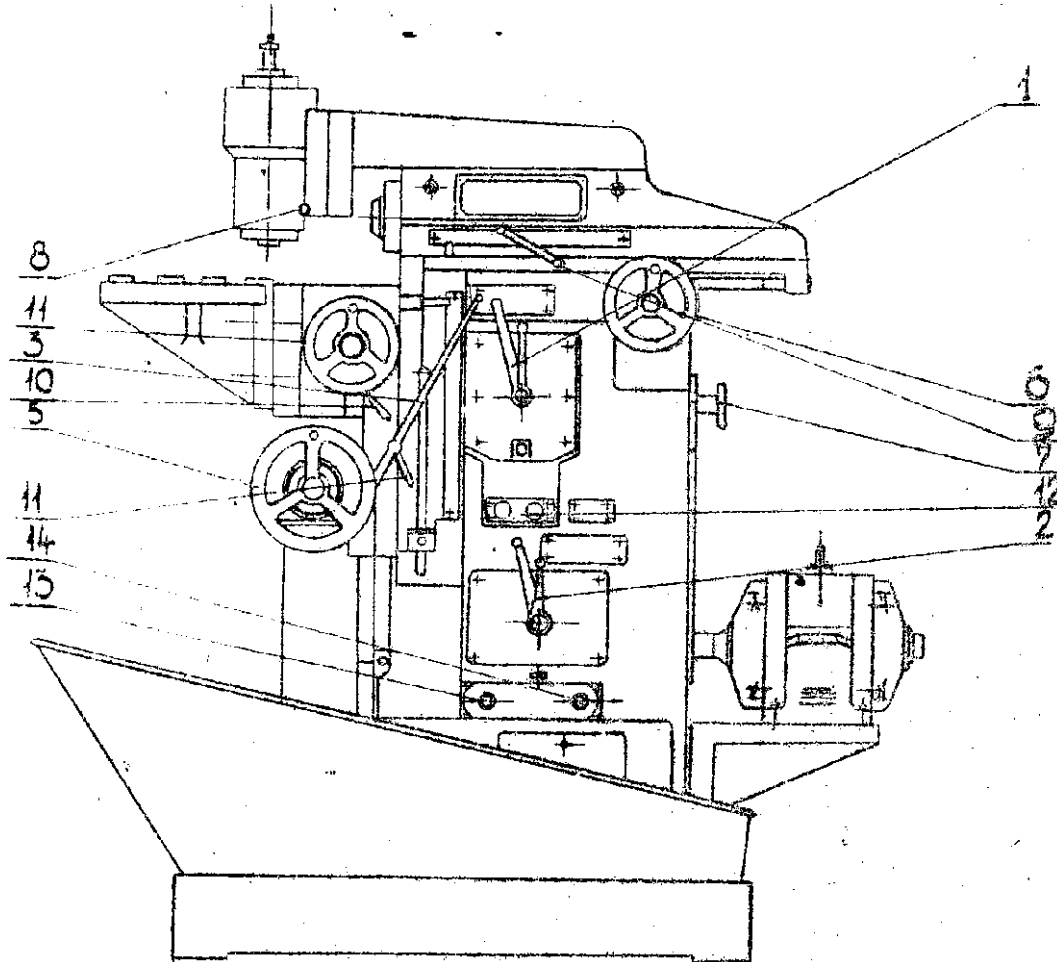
Универсально – фрезерный станок 6В75 (органы управления).
